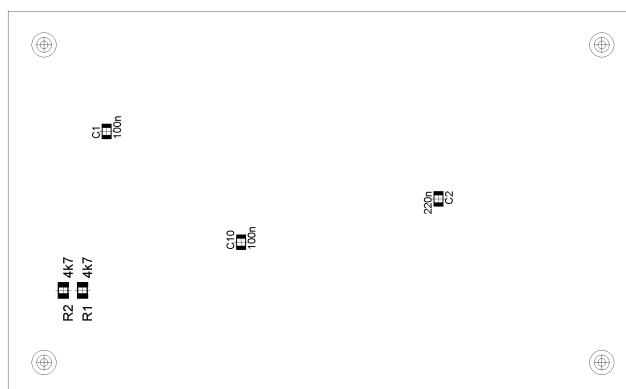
Základní deska, osazovací plán vrstva BOTTOM.
